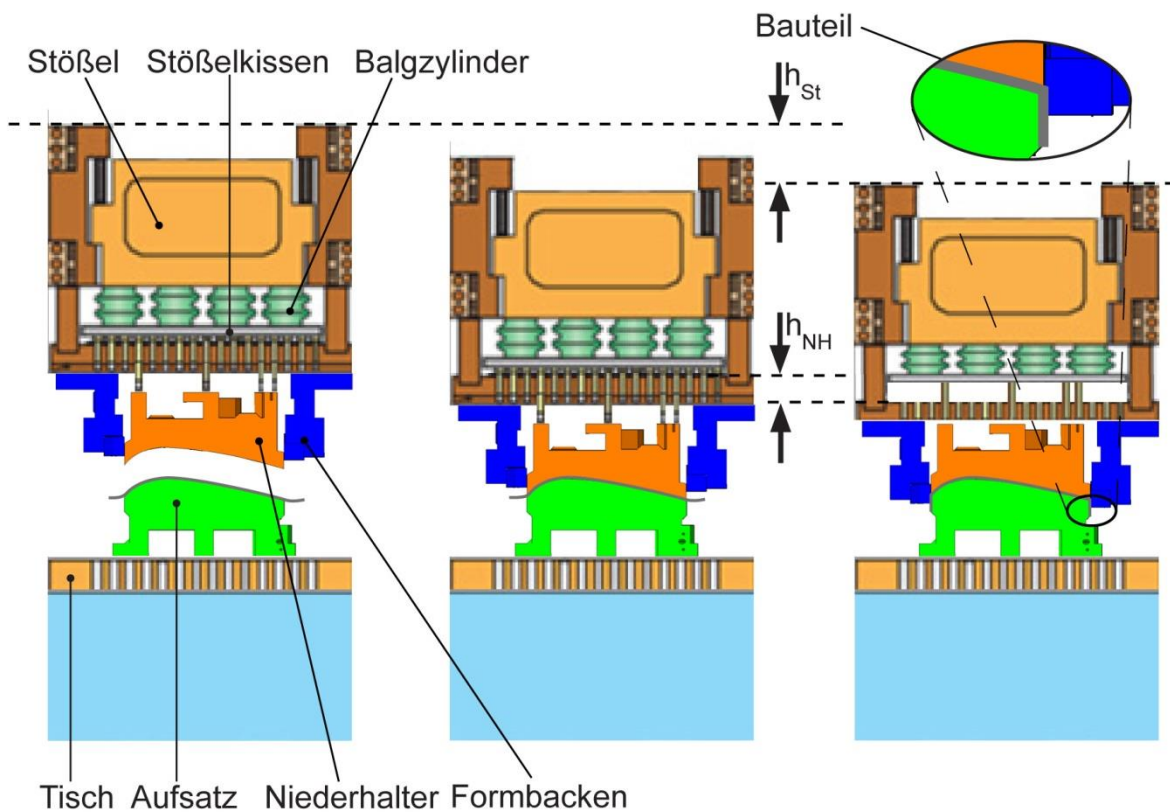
Funktionsprinzip Folgewerkzeuge für Abstellen: links geöffnetes Werkzeug, Mitte Niederhalter schließen, rechts Werkzeug in UU
